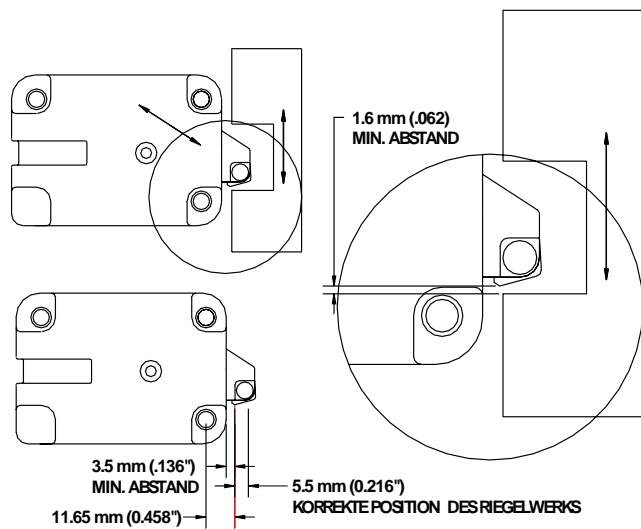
Schubriegel (Slide Bolt) mit Vierkant, Position und Toleranzen
